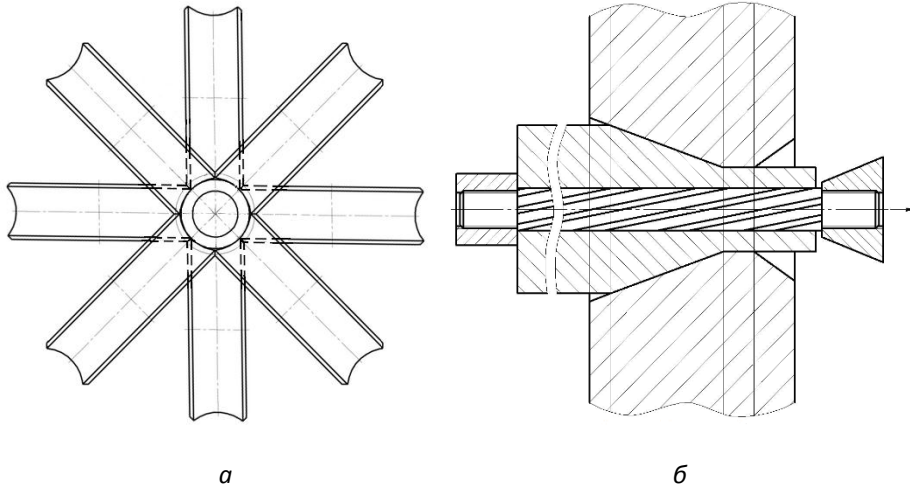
Схема обжатия ствольной заготовки: а – неприводными роликами; б – в гладкой конической матрице
